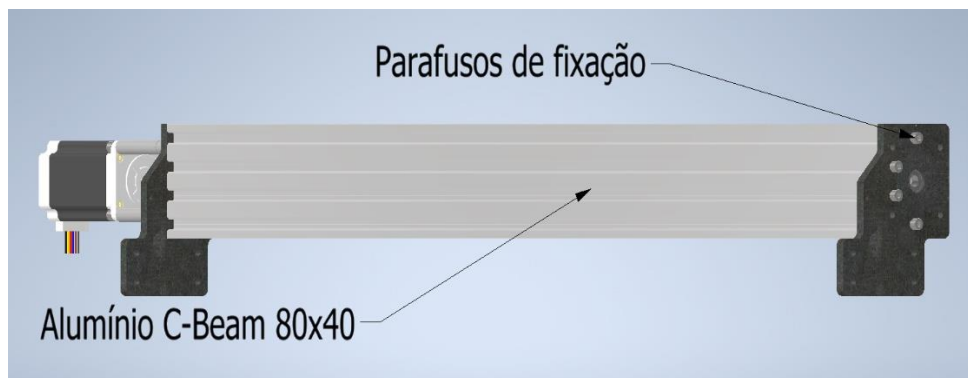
Fixação do perfil estrutural de alumínio a estrutura em aço
